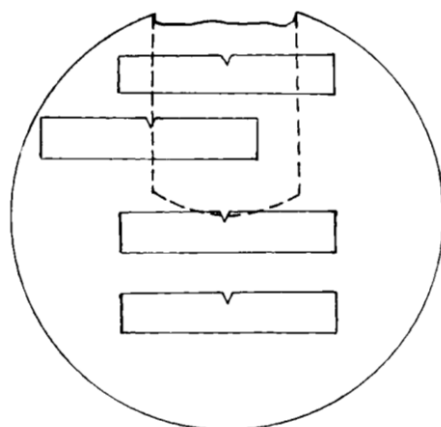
Схема вырезки образцов для ударных испытаний (KCV) из различных участков сварных соединений стали 15Х1М1ФЛ, выполненных способом поперечной горки
